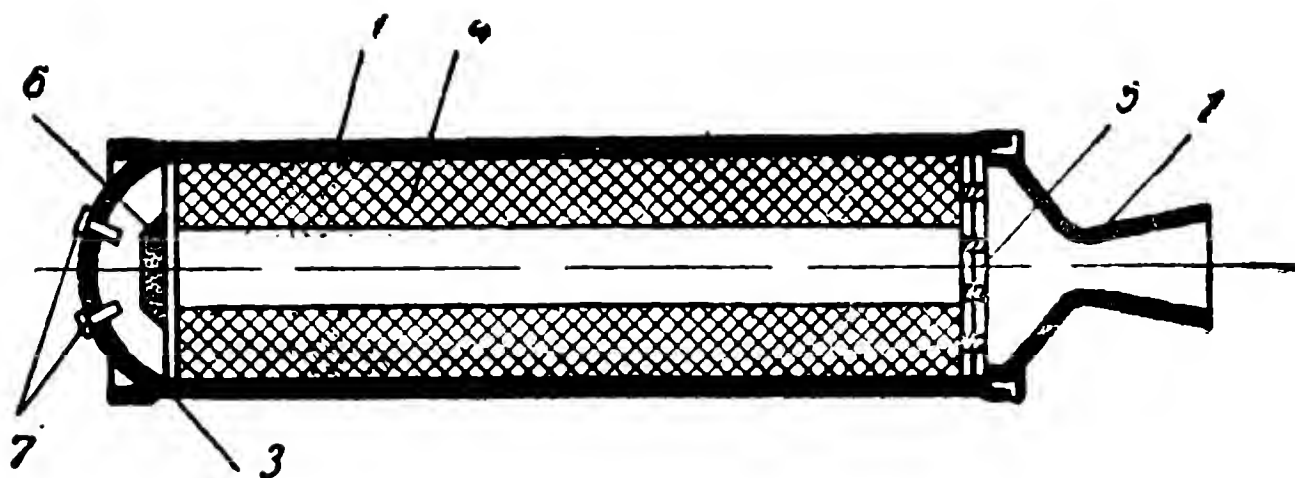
Схема устройства РДТТ: 1 — корпус камеры сгорания; 2 — сопло; 3 — передняя крышка; 4 — заряд твердого топлива; 5 — диффрагма; 6 — воспламенитель; 7 — пиросвечи
